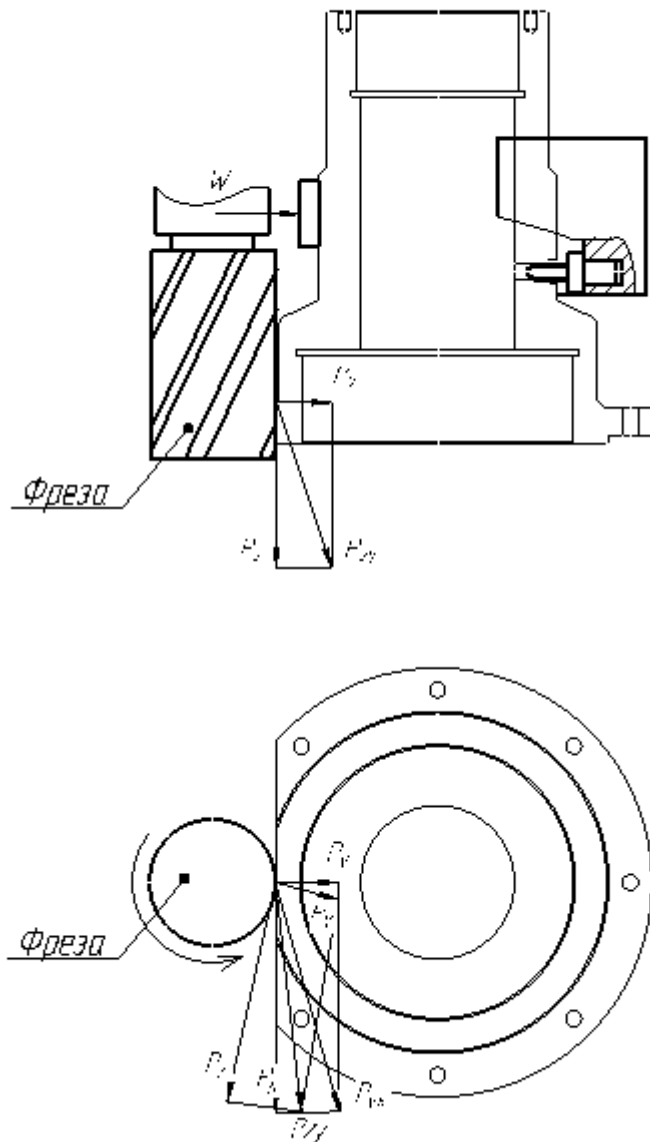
Схема для розрахунку необхідної сили затиску заготовки
